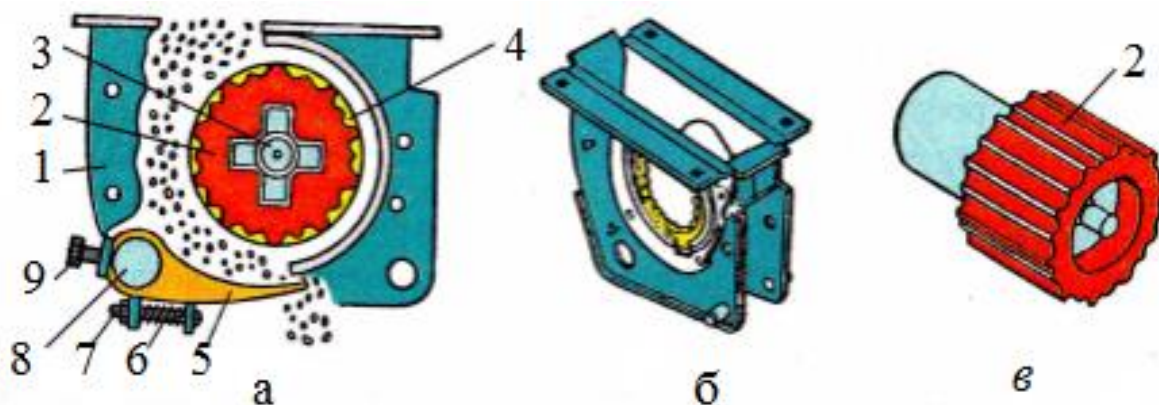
Функціональна схема (а), коробка (б) катушка (в) висівного апарата овочевої сівалки СОН-4,2: 1 – коробка; 2 – катушка; 3 – вал висівних апаратів; 4 – розетки; 5 – клапан; 6 – пружина; 7 – регулювальний болт; 8 – вал клапанів випорожнення; 9 – стопор.
